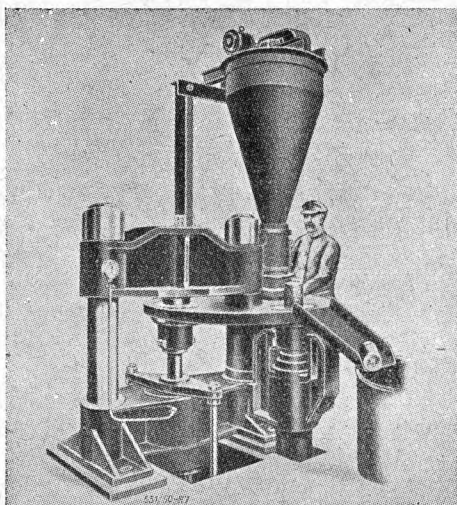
Prasa wielokierunkowa z napędem hydraulicznym wszystkich mechanizmów.
